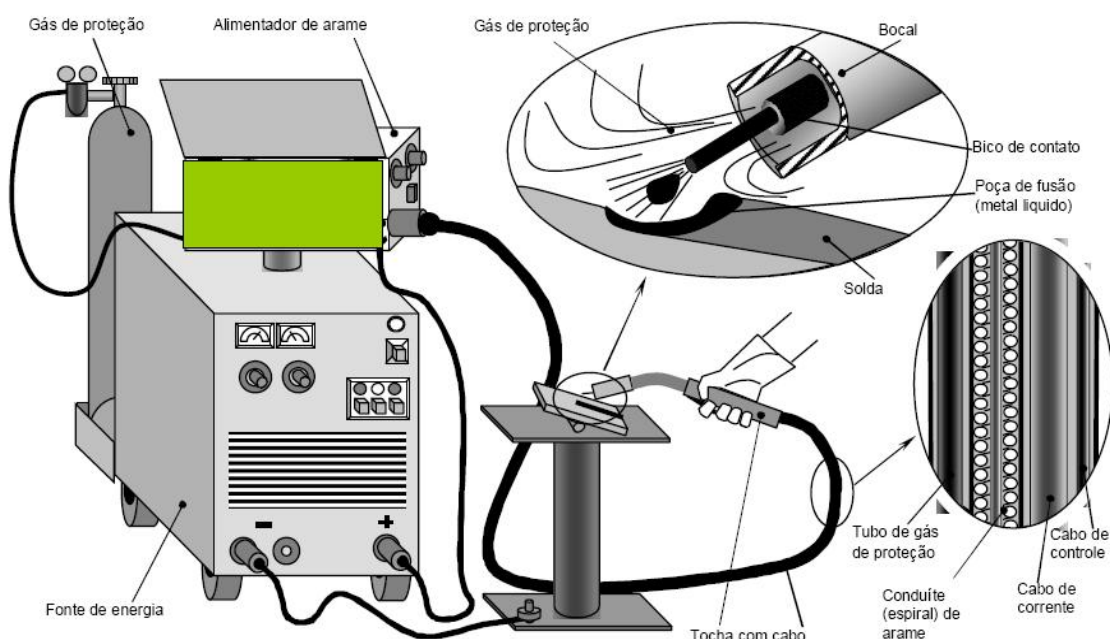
Descrição simplificada do processo de soldadura GMAW.
